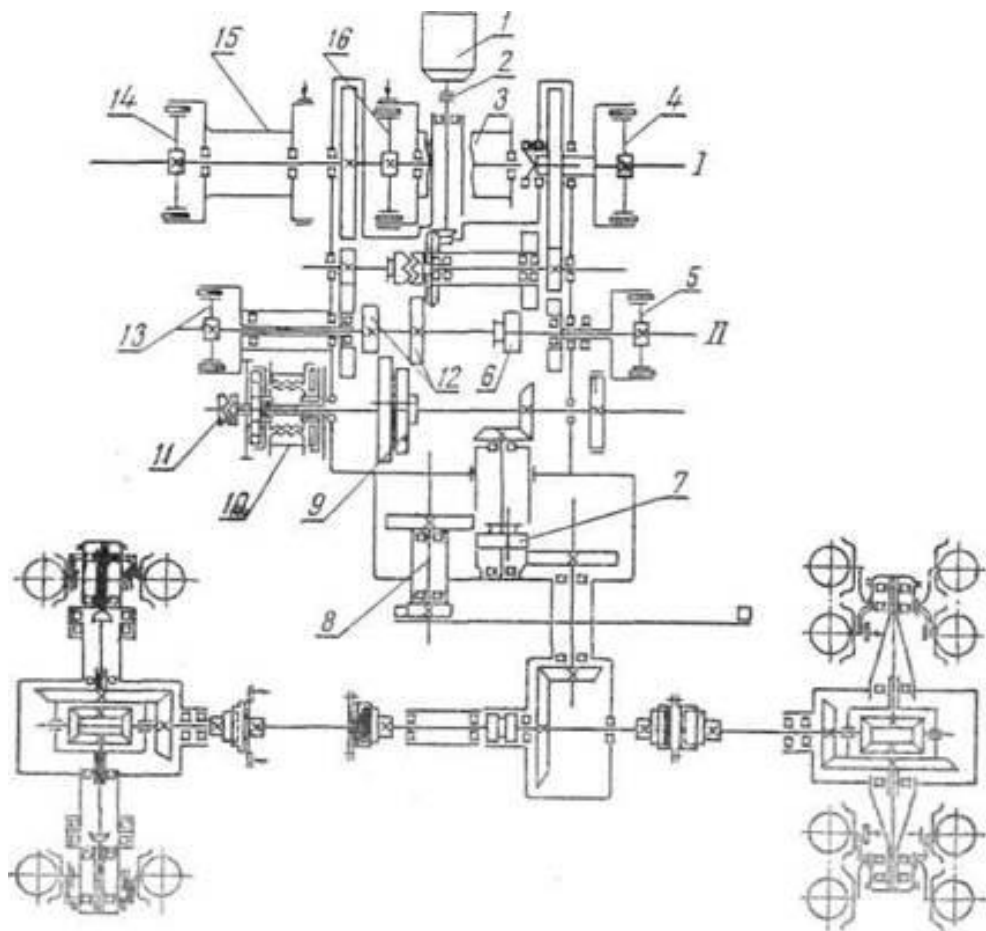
Кинематическая схема экскаватора на пневмоколесном ходу с унифицированным рабочим оборудованием:
